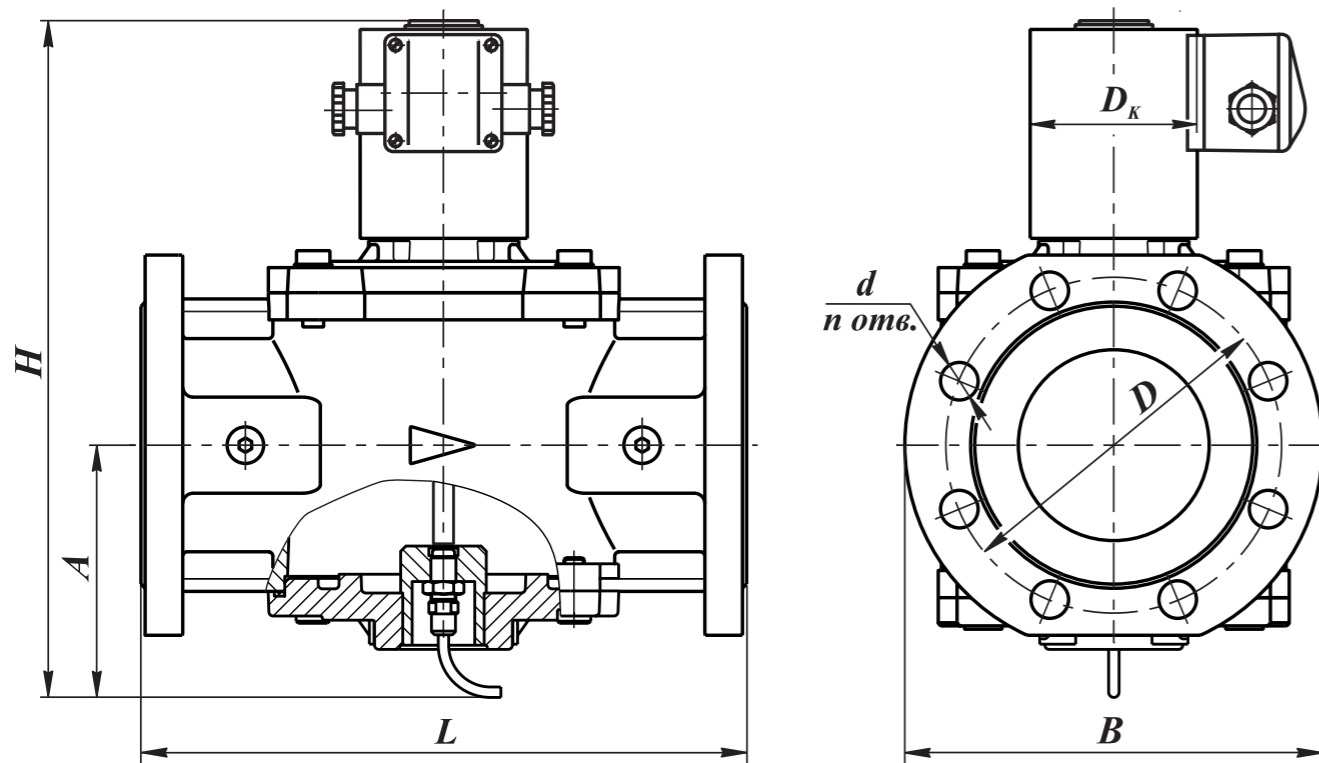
Клапаны на DN 50 - 100 фланцевые с датчиком положения (исполнение: с присоединительными фланцами PN 16)
